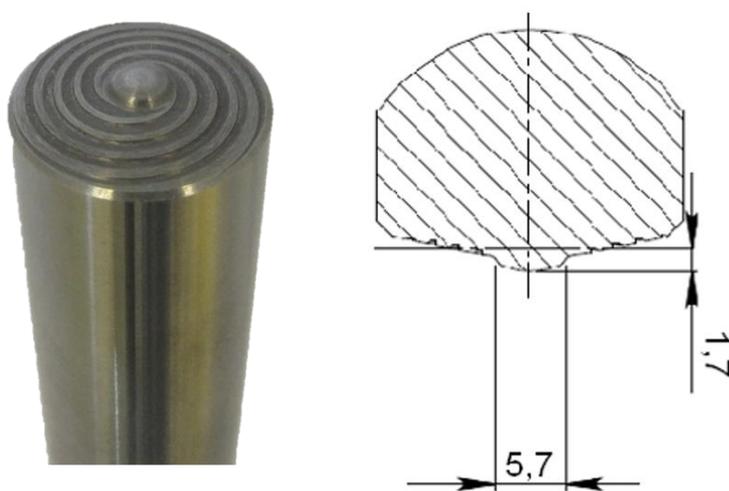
Ferramenta de WC-13%Co fabricada pela Megastir e utilizada para soldagem das chapas finas.
